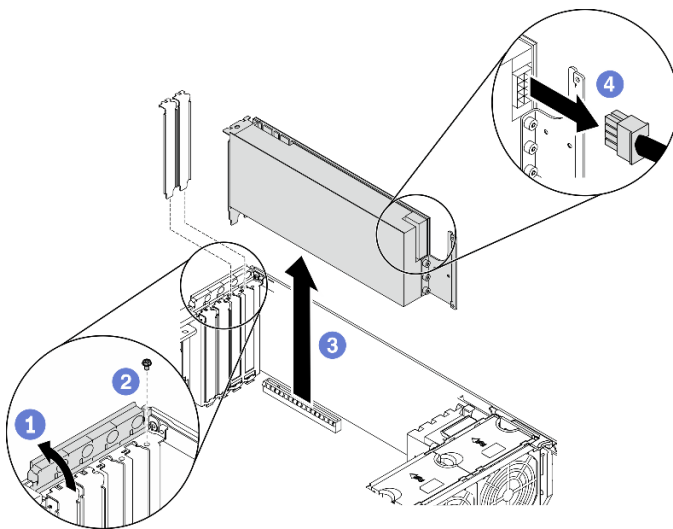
Entfernen des GPU-Adapters mit voller Länge
